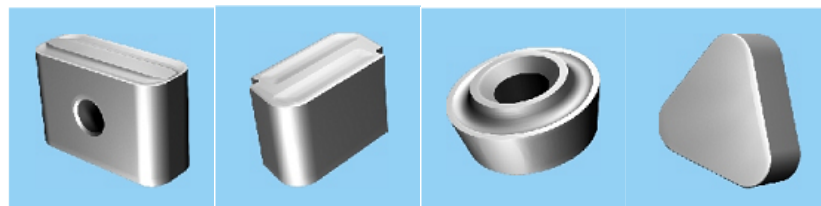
Пластини різальні (Кіровоградський завод твердих сплавів), що рекомендовані для обточування деталей на важких верстатах
